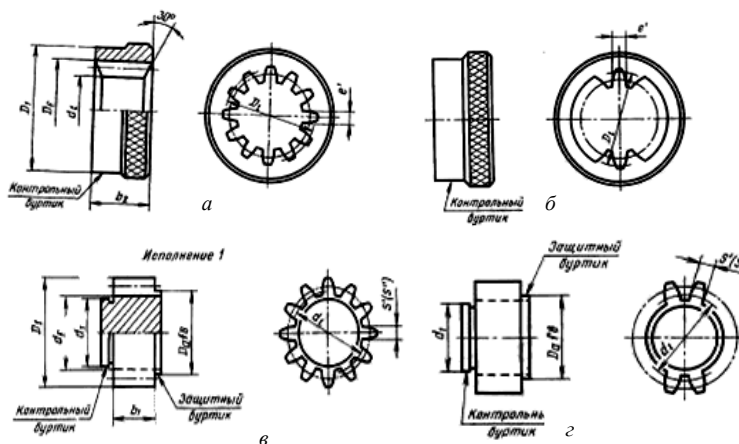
Калибры для контроля деталей эвольвентных соединений:
